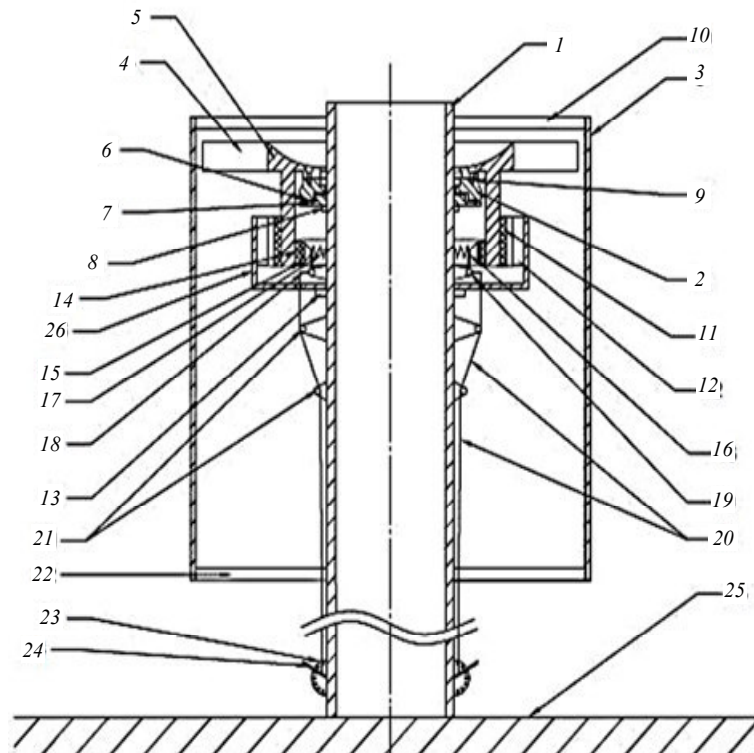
Размещение ВЭУ на верхней части дымовой трубы при расположении обмоток статора с внешней стороны (вид сбоку): 1–12 и 14–25 (см. обозначения на рис. 2, а); 13 – упорный бурт для монтажа корпуса статора; 26 – корпус статора
